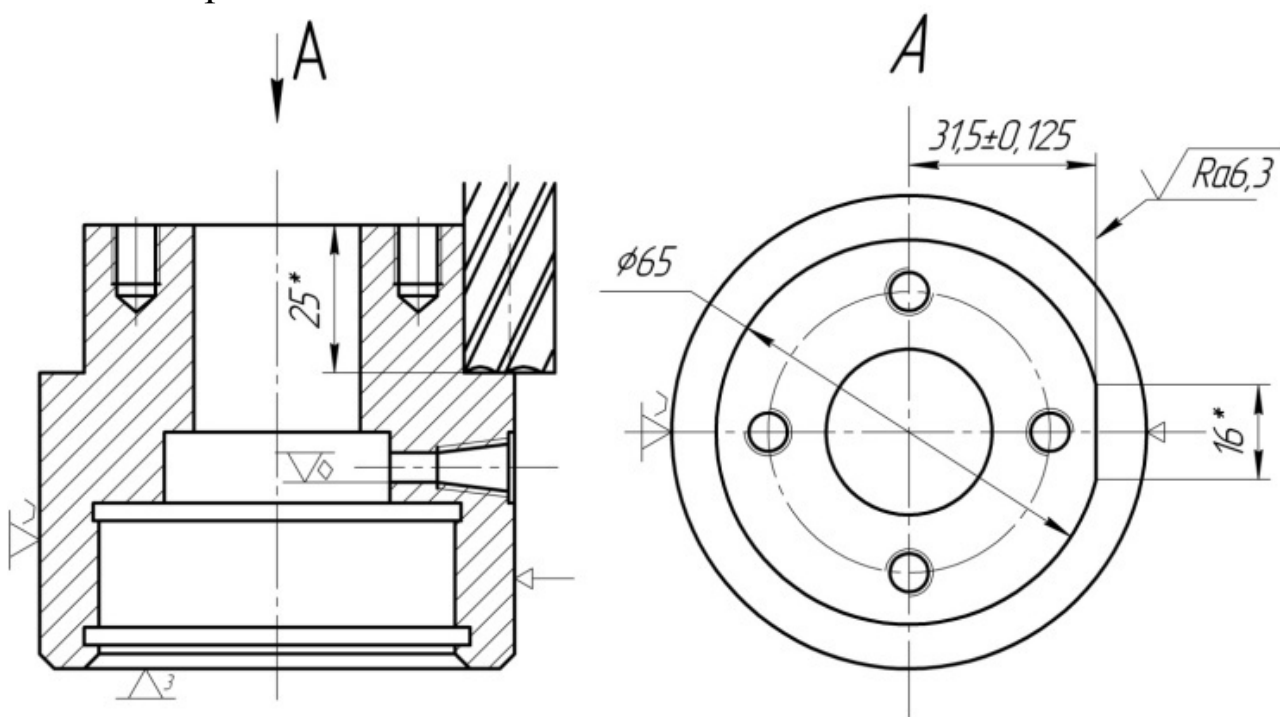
Операционный эскиз при установке заготовки на опорные пластины и призму
